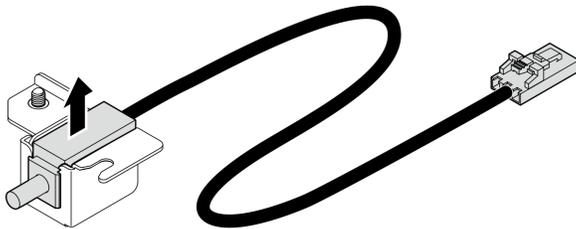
Entfernen des Schalters gegen unbefugten Zugriff
